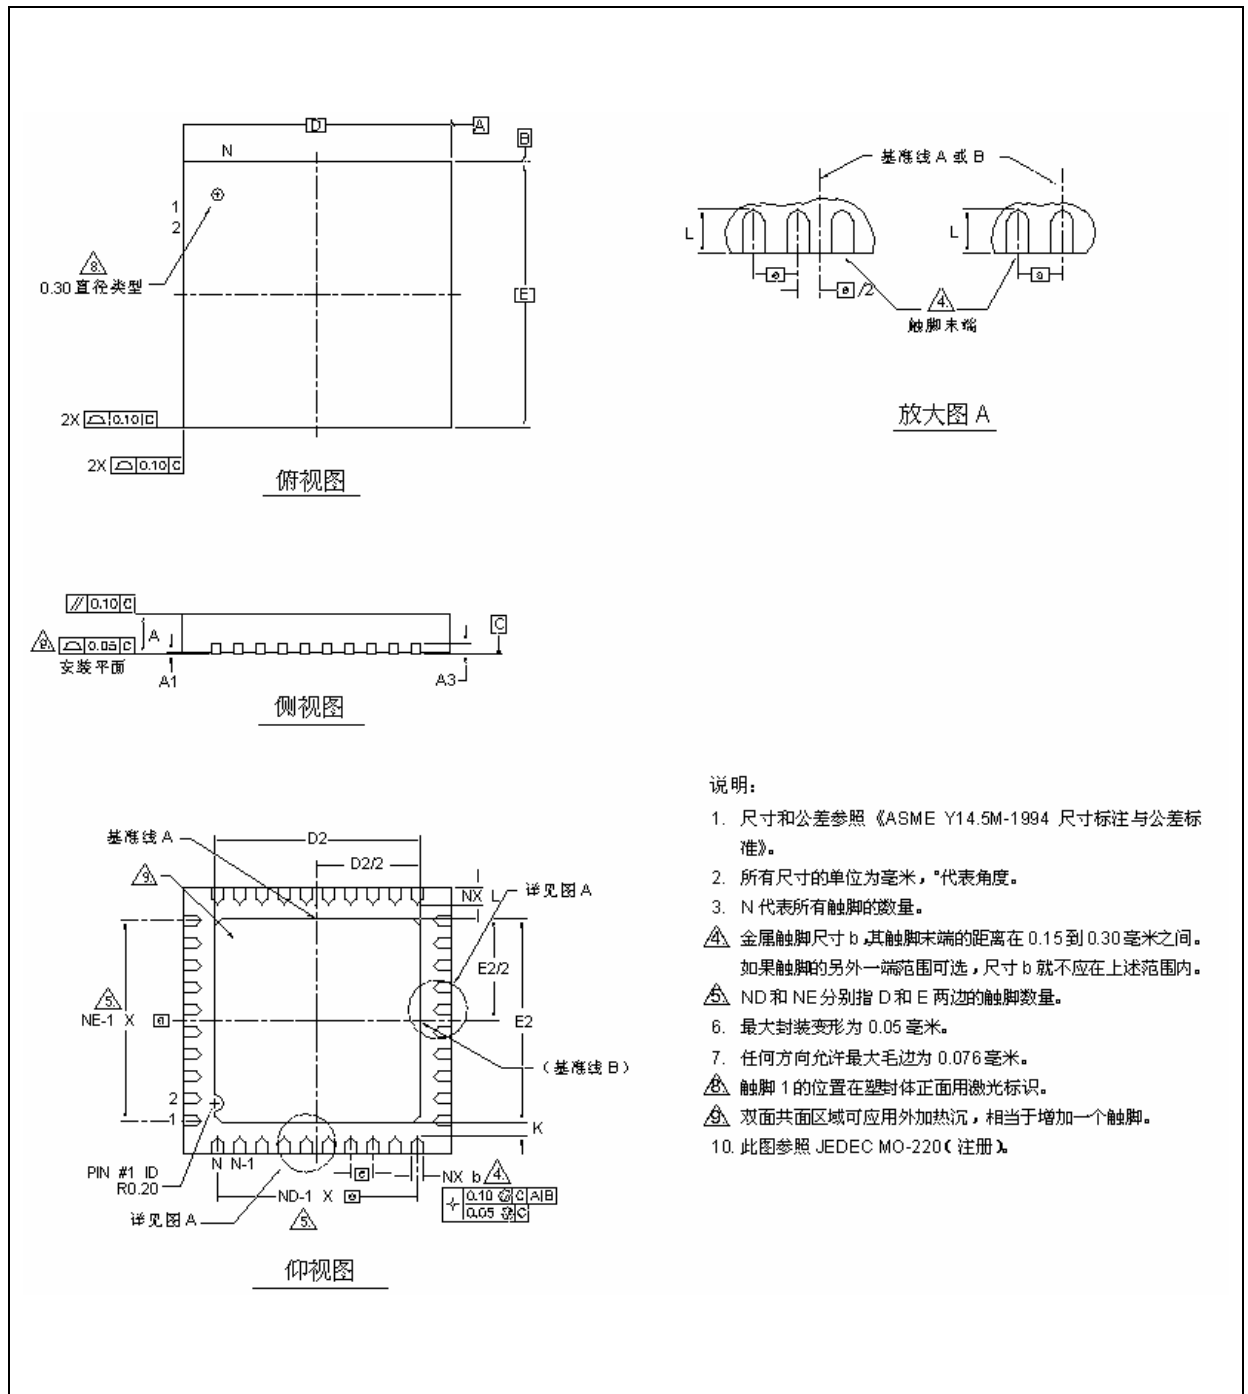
FM17XX 28 引脚 QFN 封装尺寸
